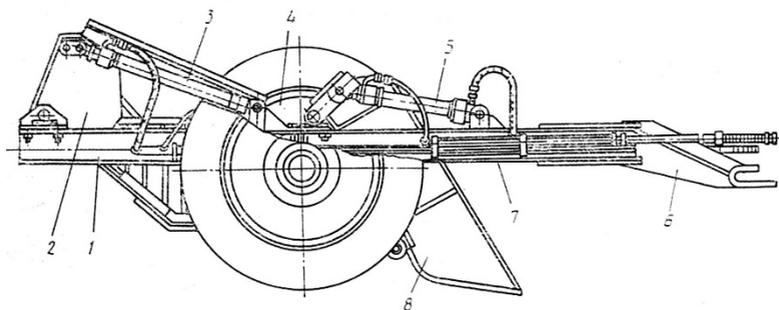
Подборщик средних камней УКП-0,7: 1 – рама; 2 – бункер; 3 – гидроцилиндр опрокидывания бункера; 4 – колеса опорные; 5 – гидроцилиндр управления гребенкой; 6 – прицепное устройство; 7 – маслопроводы; 8 – гребенка
